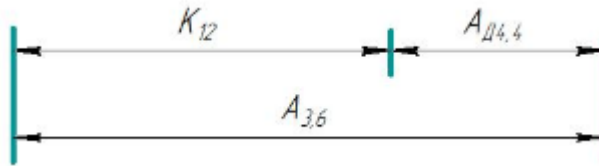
Размерная цепь для проверки конструкторского размера  $K_{12}$
